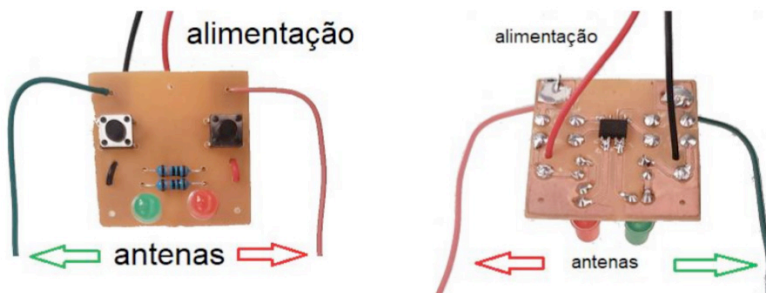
Placa de circuito impresso do novo CBC com componentes eletrônicos instalados.
